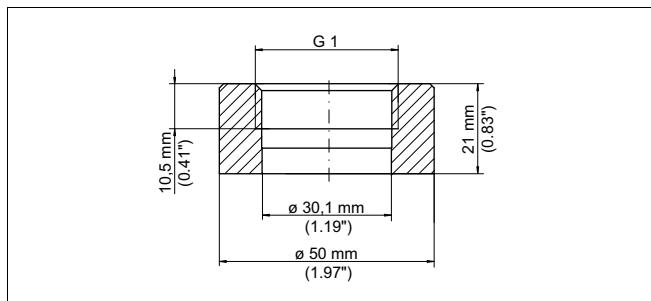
Размеры приварного штуцера G1 В по ISO 228-1
